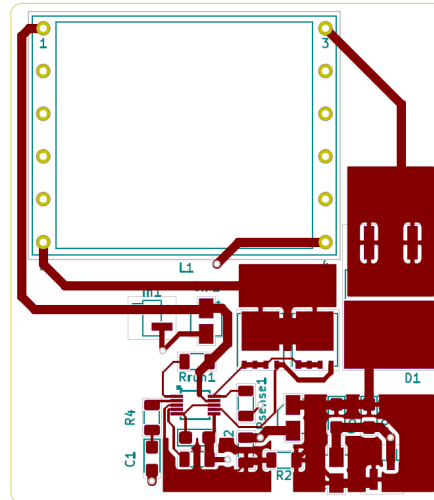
Diseño de PCB mostrando únicamente las pistas frontales.
